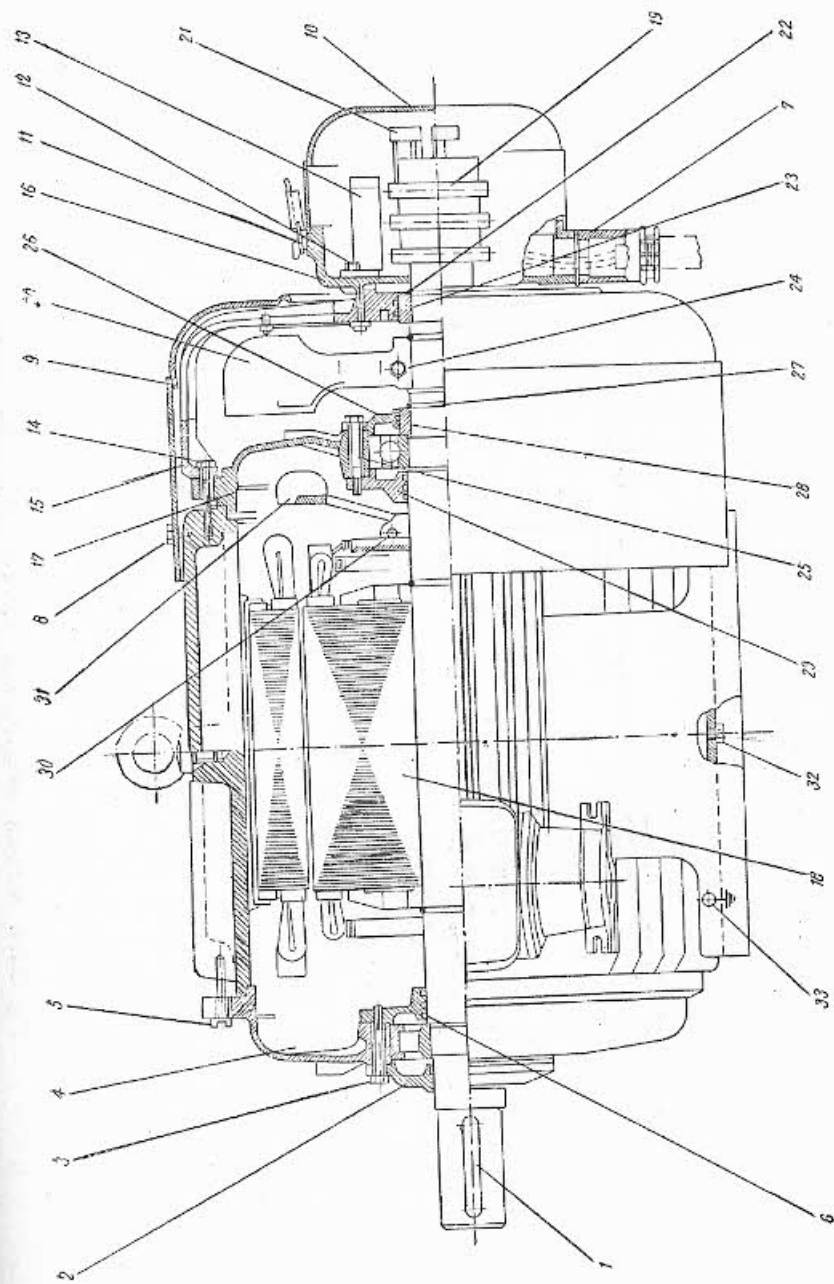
Secțiune printr-un sector asincron cu rotorul bobinat și cu inele colectoare.
